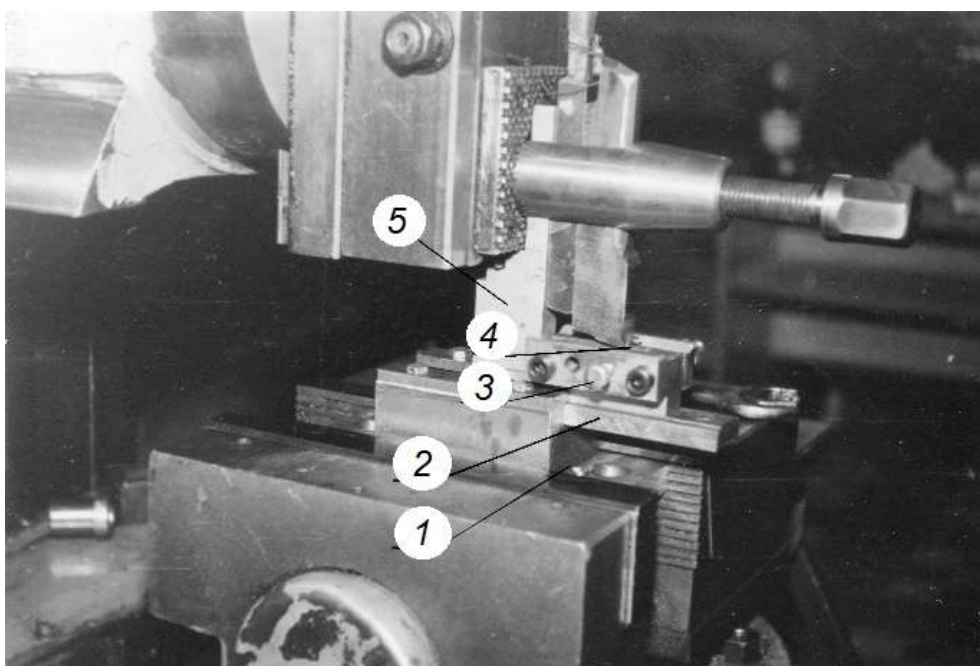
Приспособление для мгновенного прерывания процесса резания
